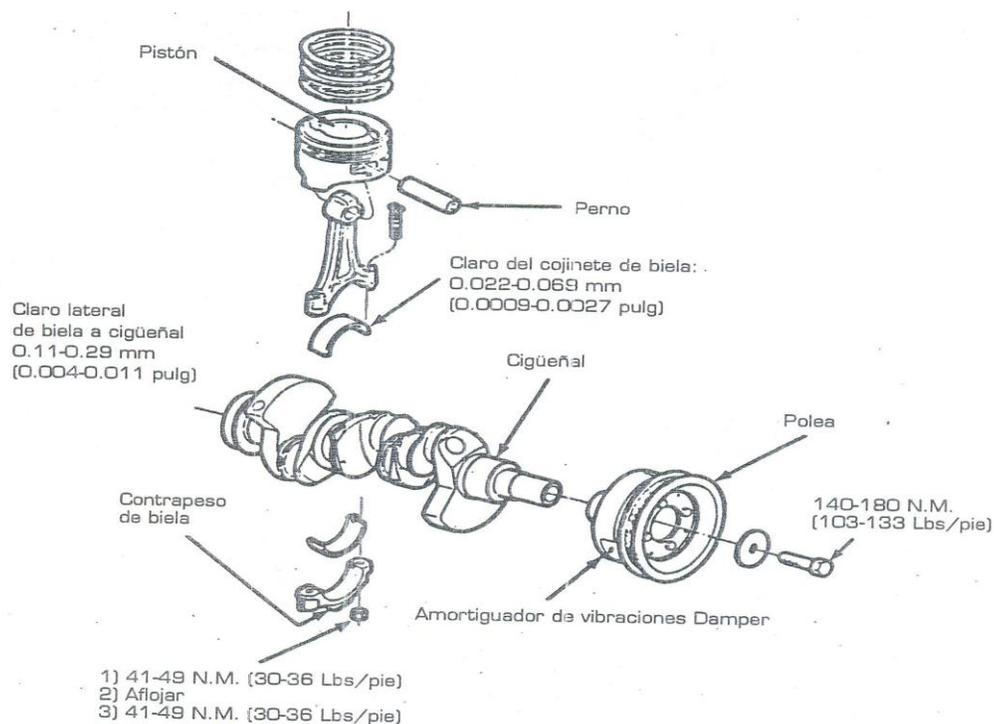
Ensamble y Componentes del Cigüeñal.
